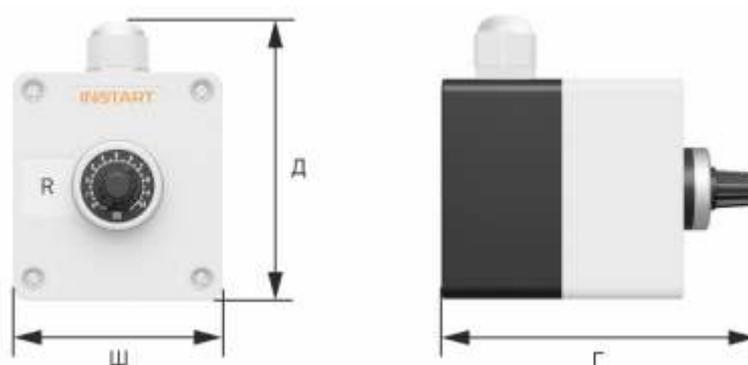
габаритные размеры ПУ-1-Х Y Z
